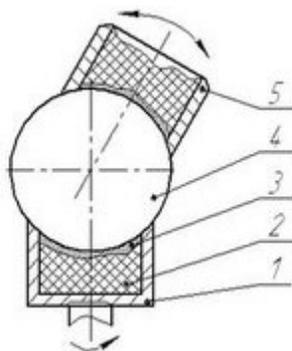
Схема шлифования шара трубчатым инструментом
